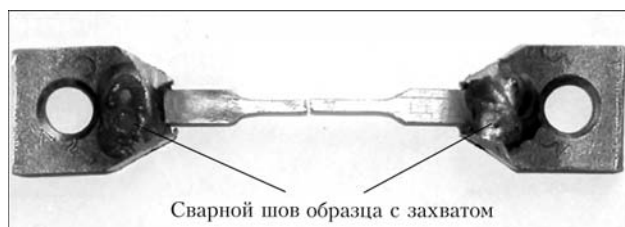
Внешний вид составного сварного образца после испытаний на кратковременные механические свойства
